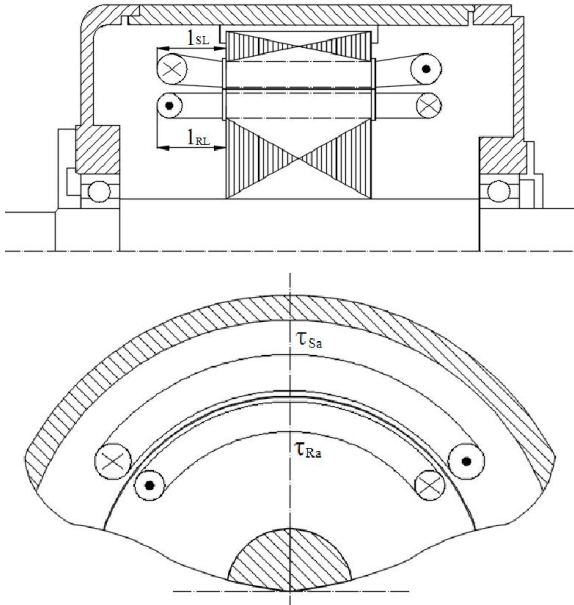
Fragmente de motor asincron cu rotor bobinat desfășurat în plan.
